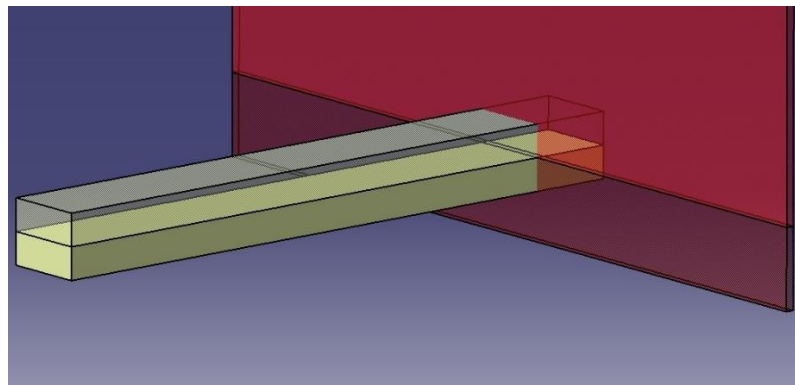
Disposition des éléments transparent (PEKK 6002 amorphe) et opaque (PEKK 6002 Semi-cristallin) pour le soudage laser par transmission
